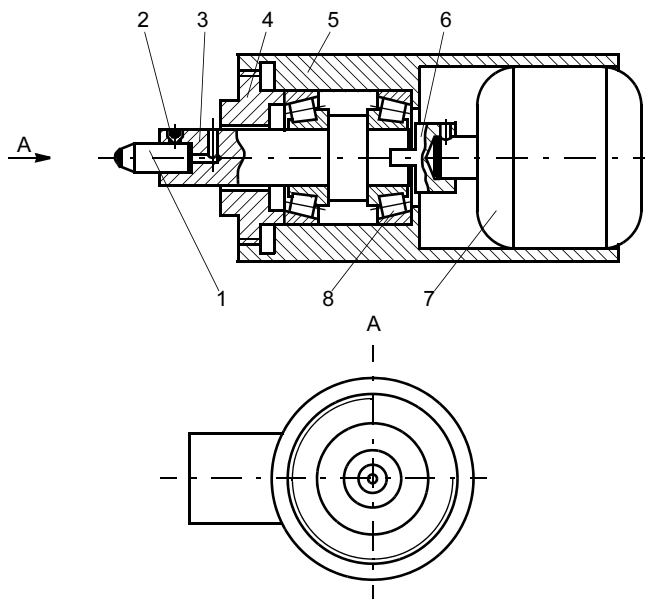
Сферический шлифовальный круг для обработки наружных поверхностей деталей — тел вращения
